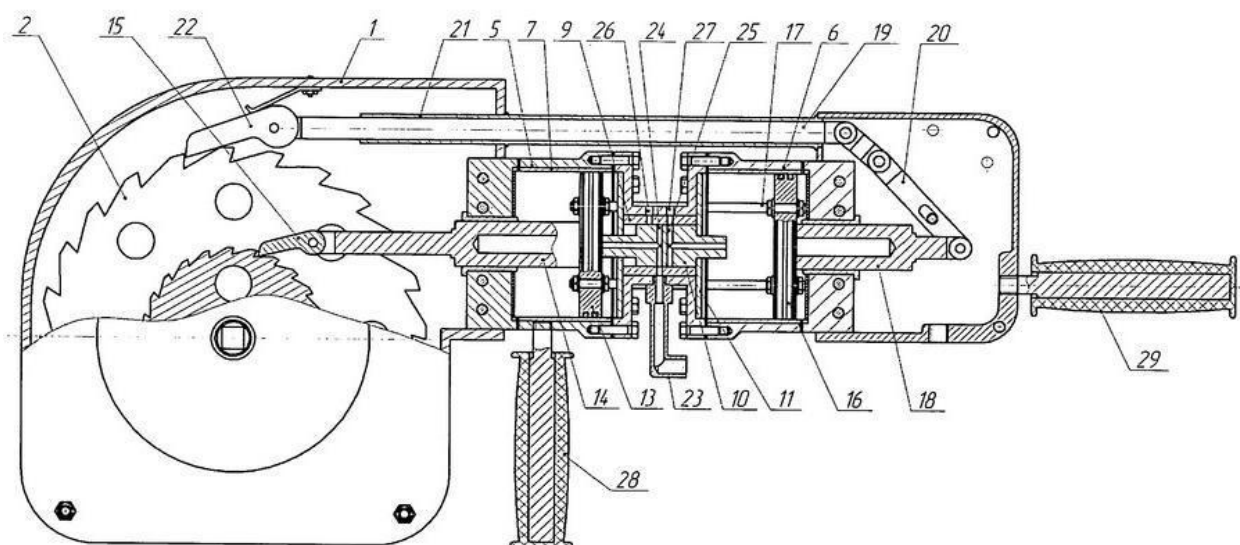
Гайковерт пневматический с храповым колесом (патент РФ 2510614)
